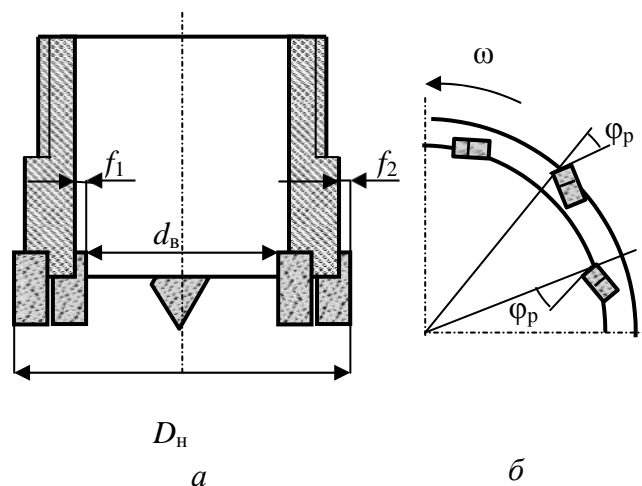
Схема вооружения твердосплавной коронки: *a* – вид сбоку в разрезе; *б* – размерещение резцов на торце коронки с поворотом на угол φ_p в фронтальной плоскости резания-скалывания
